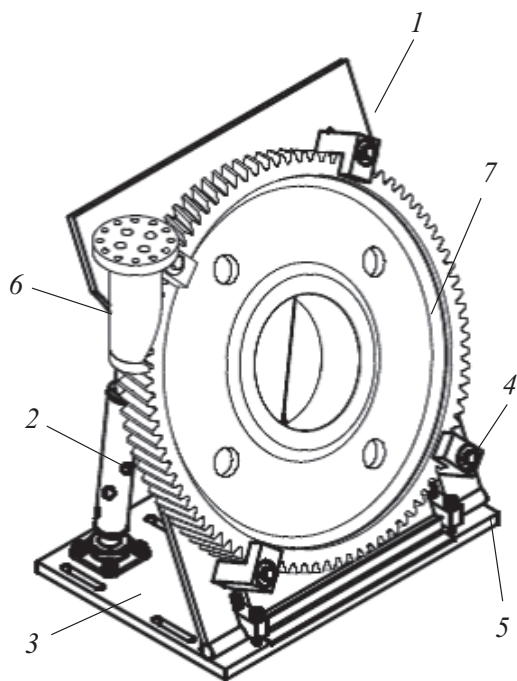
Специальное приспособление для закрепления и создания нагрузки при испытаниях зубьев зубчатых колес на изгиб: 1 – лист наклонный; 2 – винт с проушиной; 3 – лист нижний; 4 – прижим; 5 – полухомут; 6 – нагрузочное приспособление; 7 – зубчатое колесо
